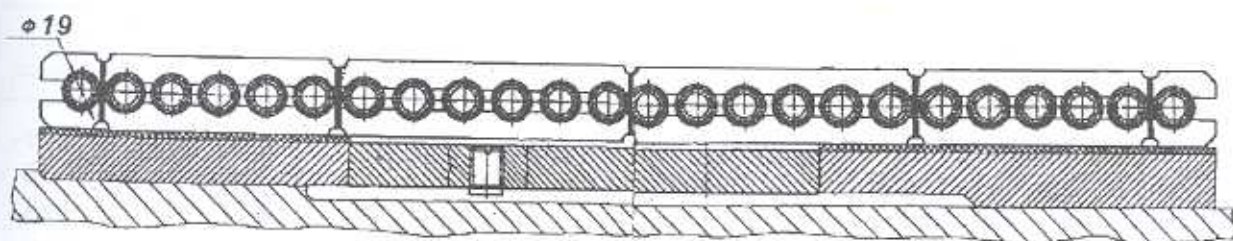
Установка индуктора для нагрева втулки контактного кольца
